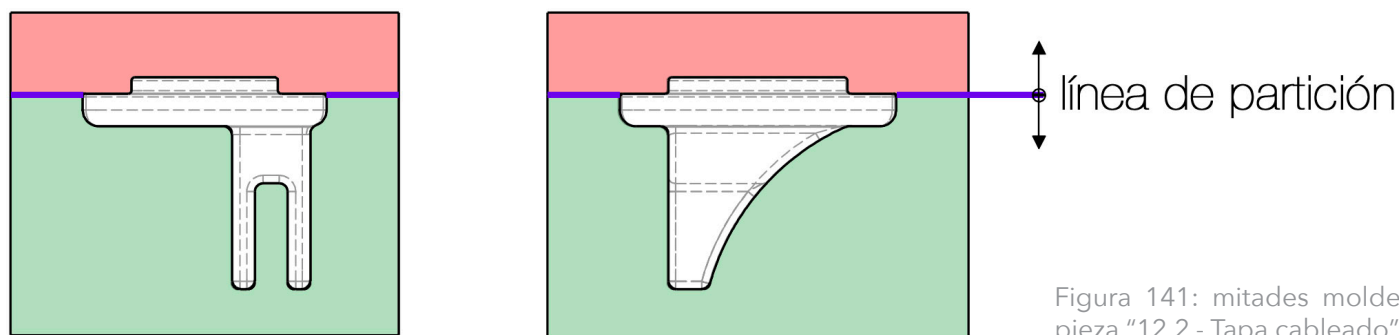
mitades molde pieza "12.2.- Tapa cableado"
